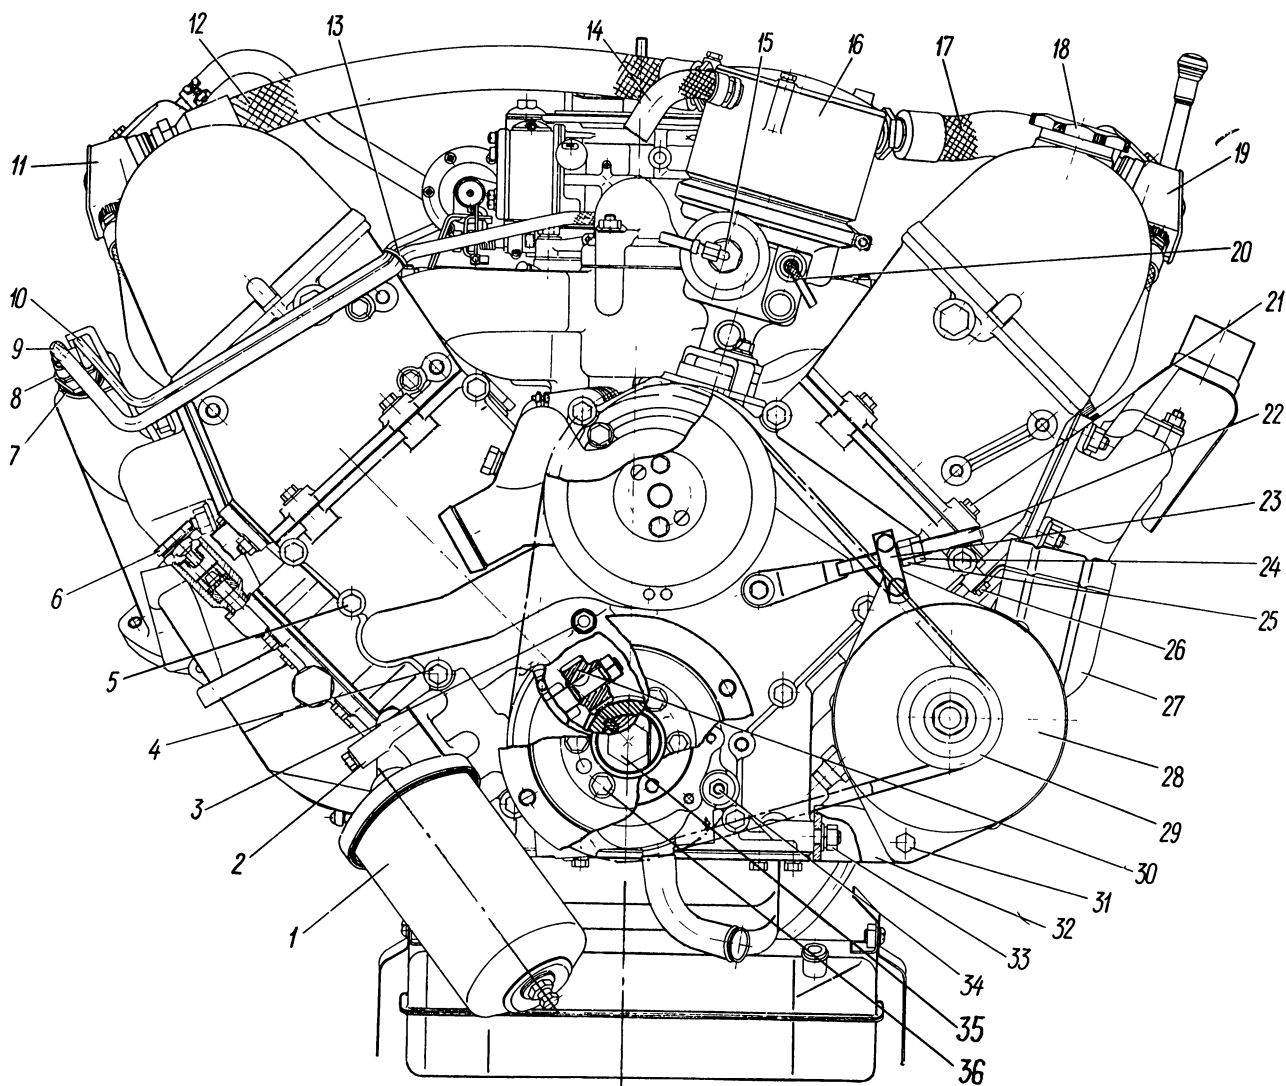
Двигатель ЗИЛ-4104 (вид спереди)
